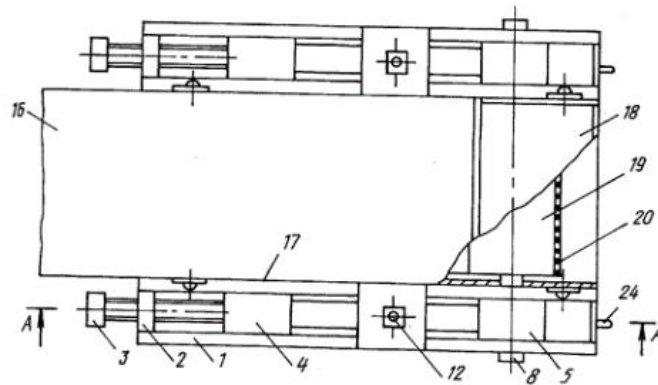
Конструкція натяжного пристрою за патентом RU № 2214355
